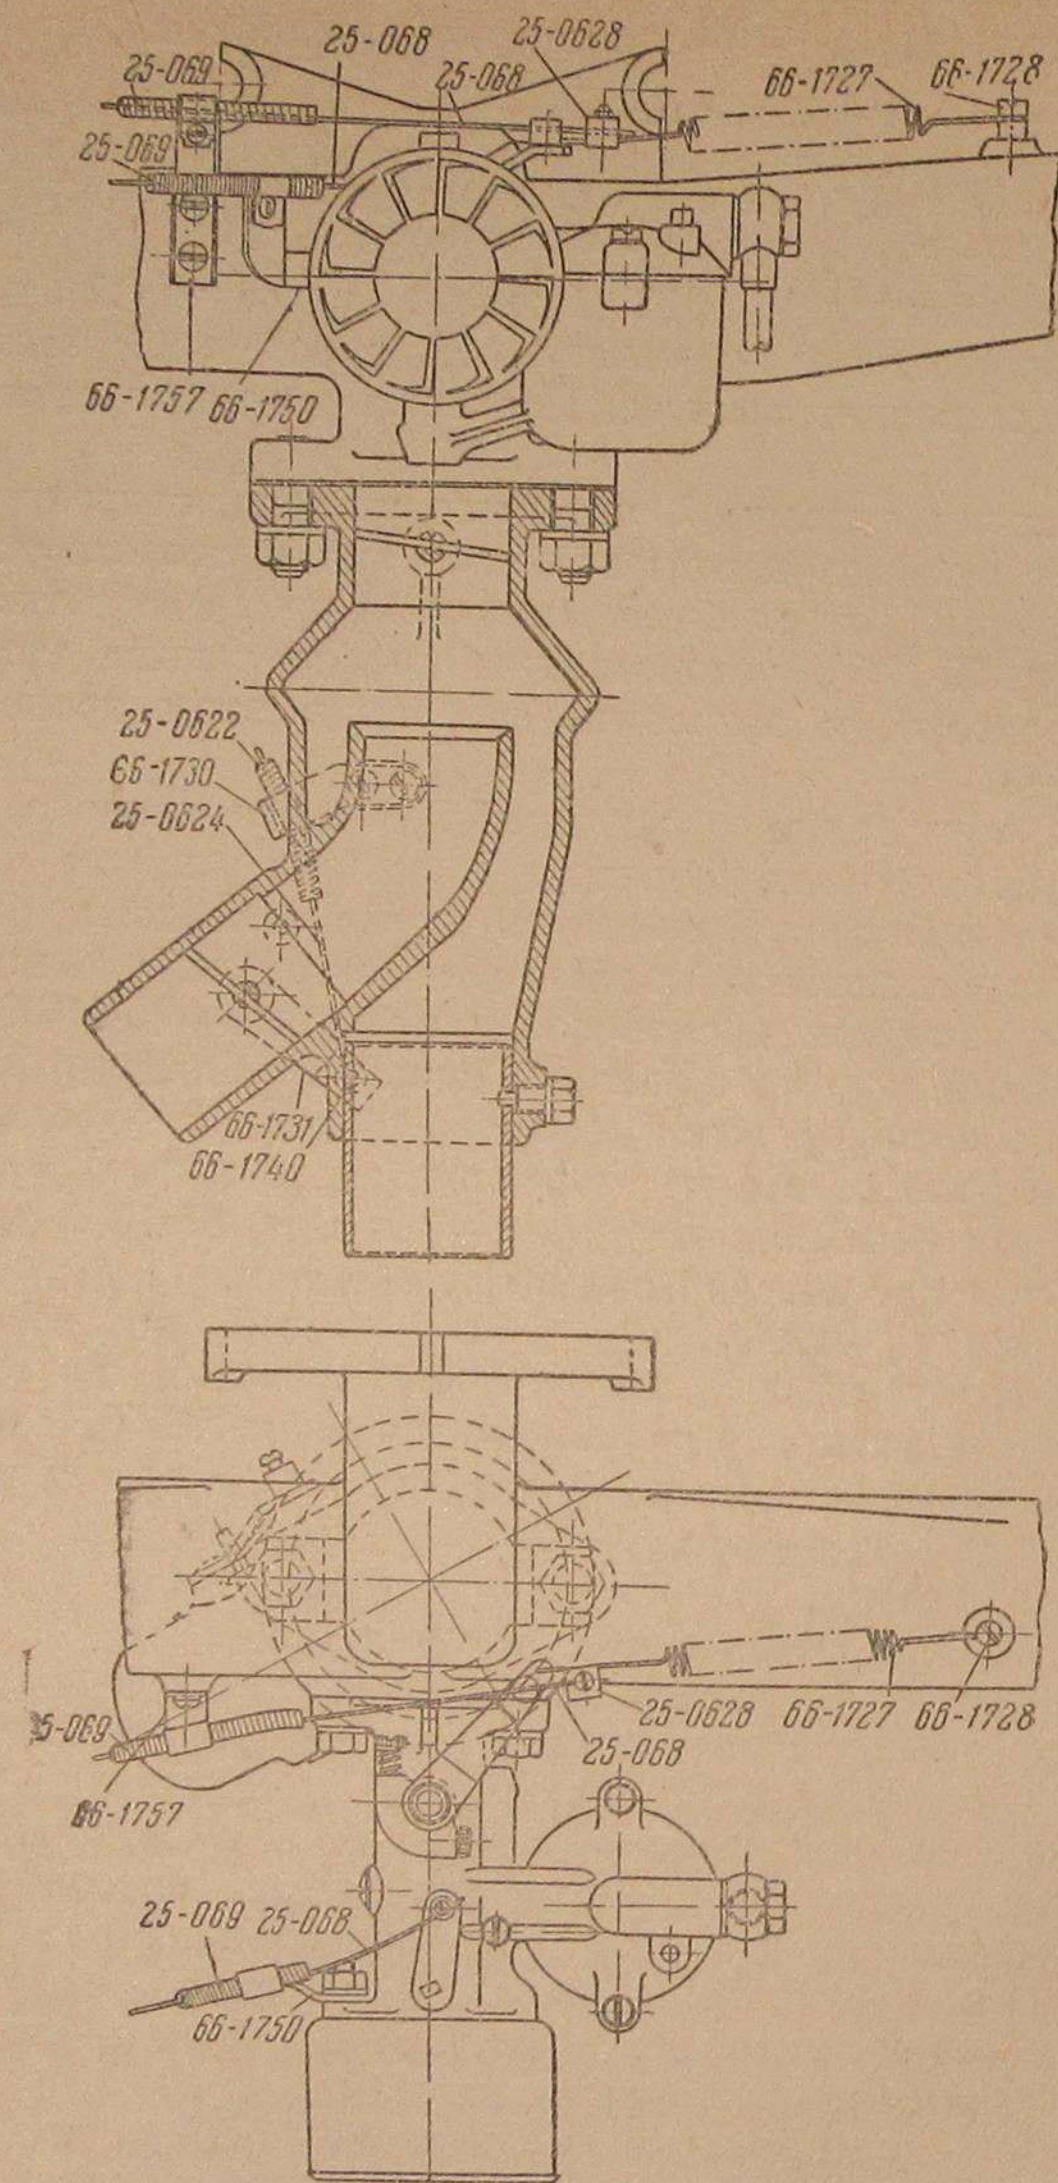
Установка и крепление гибких тросов управления заслонками смесителя и карбюратора
